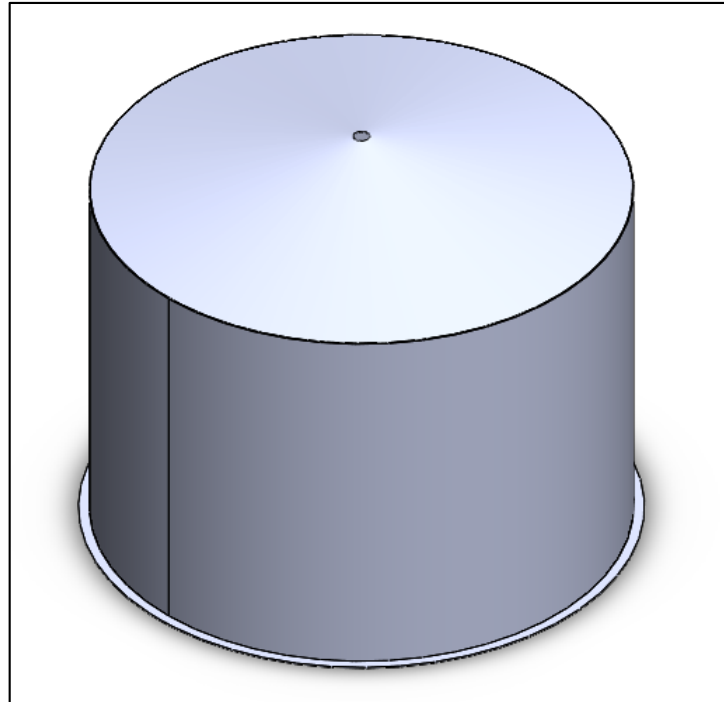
, Diseño de tanque de 12 m³ en SolidWorks.
